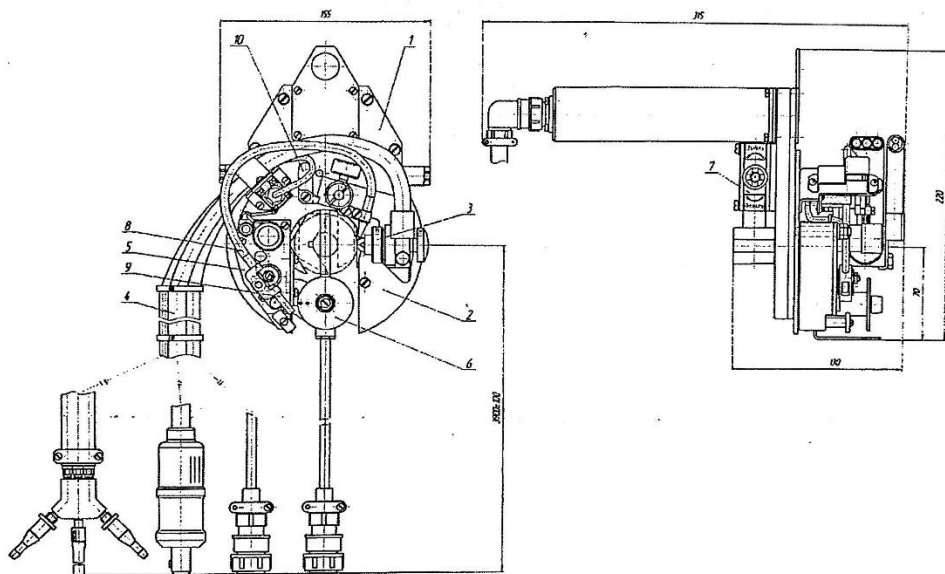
Головка сварочная ОКА 18-45 ИД [20]
